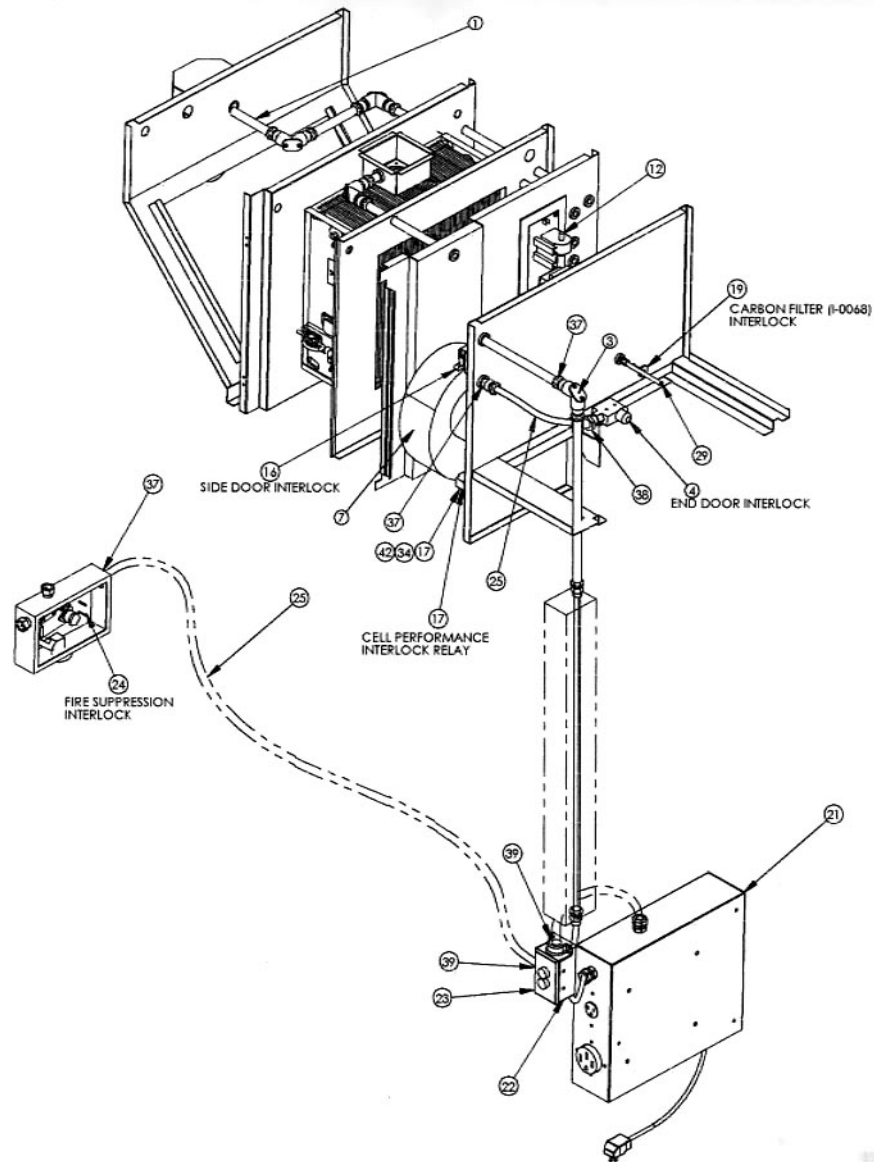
ENSAMBLAJE ELECTRICO DEL INSIDER.
